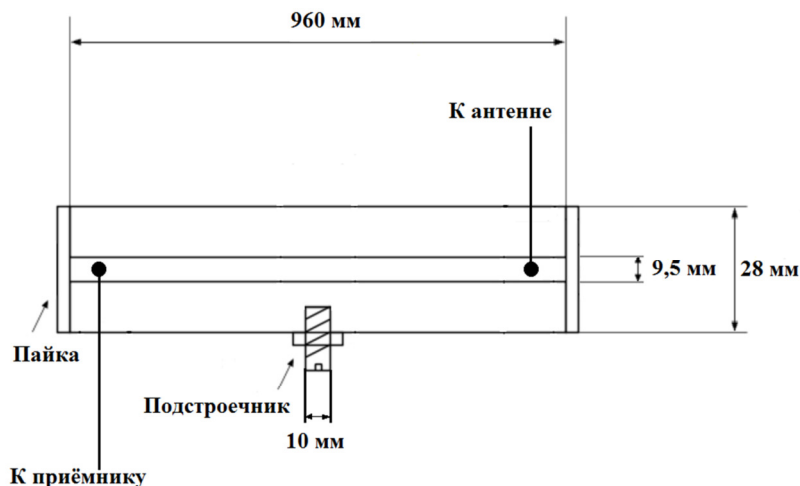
Устройство полуволнового полосового фильтра – резонатора
